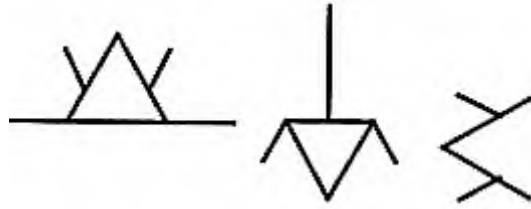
Условные обозначения опоры, зажима и неподвижного центра с рифленой поверхностью [8]
